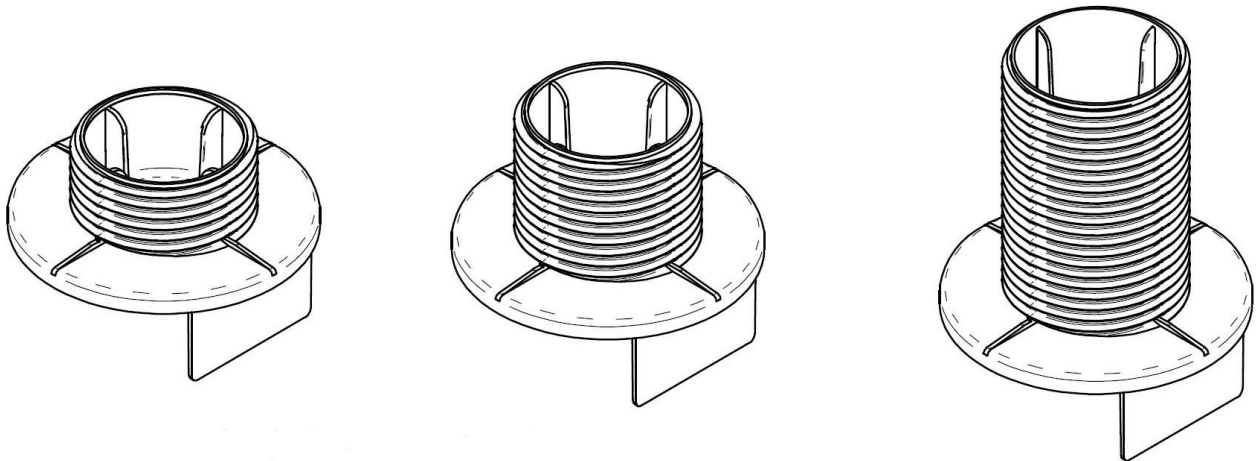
Vis lambourdes Z103064LAMB (à gauche), Z103065LAMB (milieu) et Z103066LAMB (à droite)
